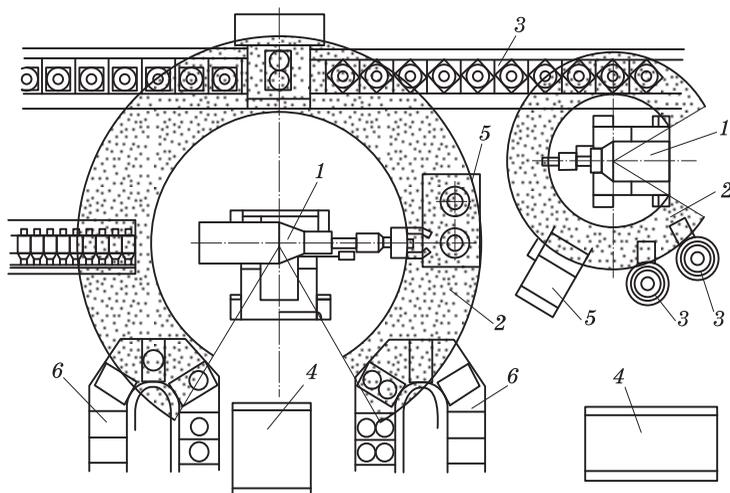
Пример компоновки роботизированного сборочного модуля: 1 — робот; 2 — рабочая зона робота; 3 — подающие устройства; 4 — рабочий; 5 — сборочные позиции; 6 — транспортеры
